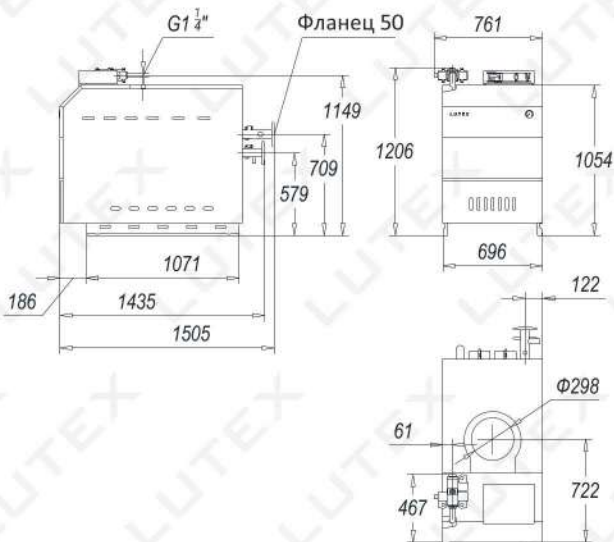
Габаритно-присоединительные размеры AR-S200
